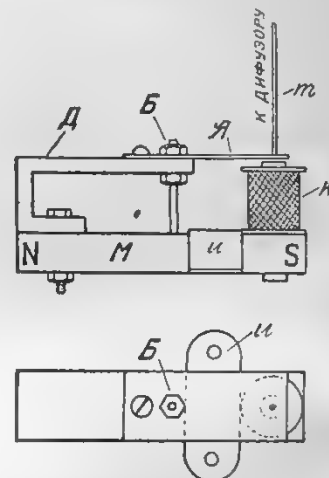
Самодельный механизм говорителя с поляризованным вибратором. М — магнит, Д — железная стойка, Я — железный вибратор, П — латунная скоба, К — катушка 6000 — 7000 витков пров. 0,05 — 0,06, В — регулировочный винт, Т — тяга к диффузору.
